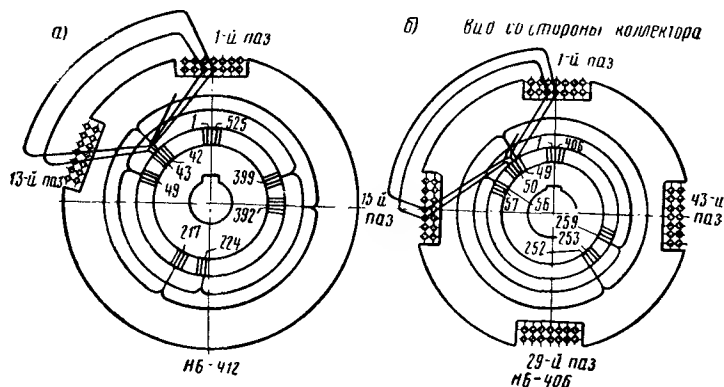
Схема соединения катушек якоря и уравнивателей с коллекторными пластинами тягового двигателя:
